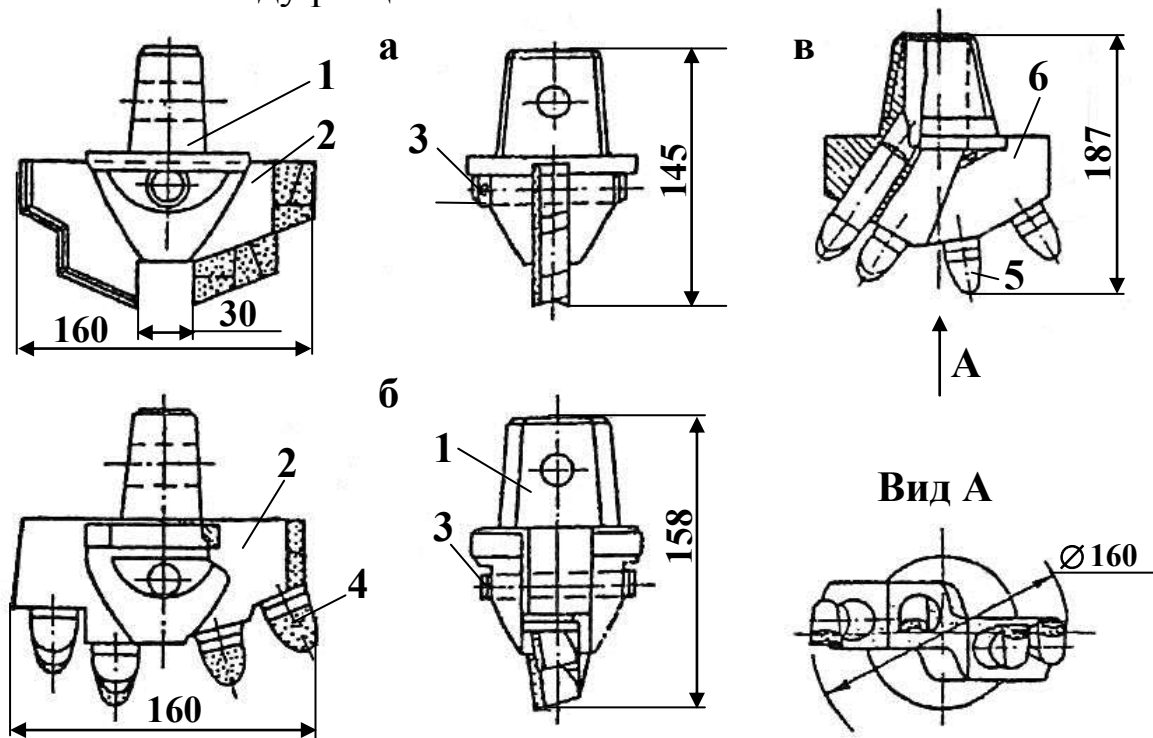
Режущие долота для бурения со шнековой очисткой скважин: а – РК4М; б – 8РД160Ш; в – 10РД160ШП (1 – хвостовик; 2 – съемный корпус; 3 – соединительный палец; 4 и 5 – резец типа ШБМ2С укороченный; 6 – литой корпус)
